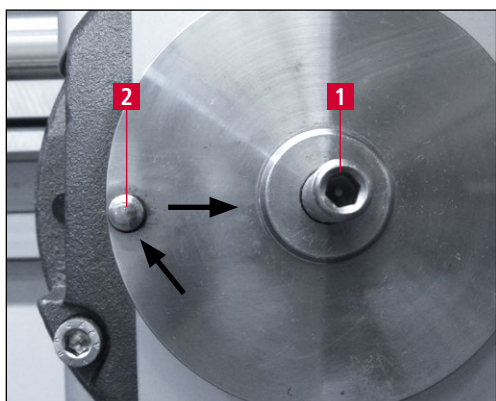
Центрирующий буртик и центрирующий штифт
